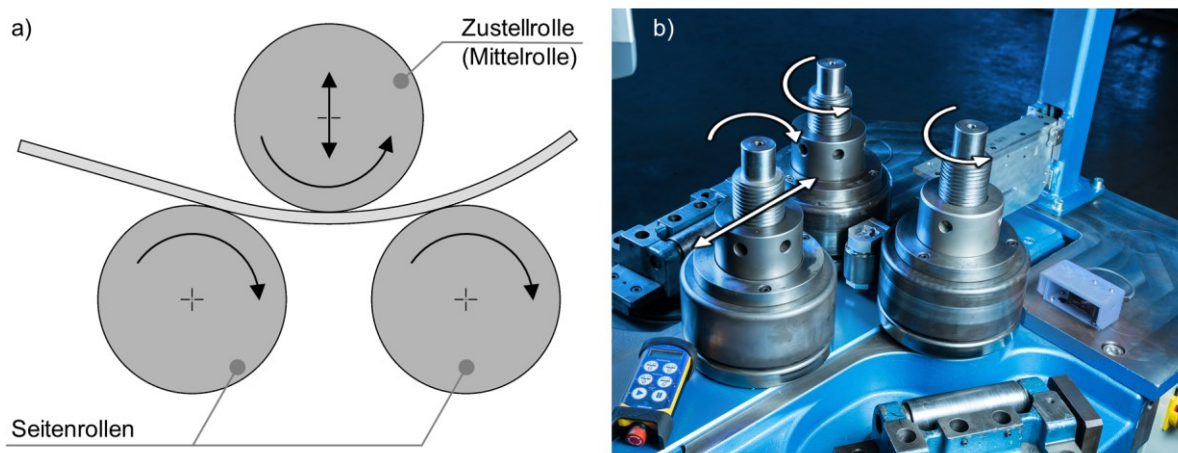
Drei-Rollen-Biegen: a) Verfahrensprinzip, b) Biegemaschine BO229 mit Universalrollensatz [HER22b]
